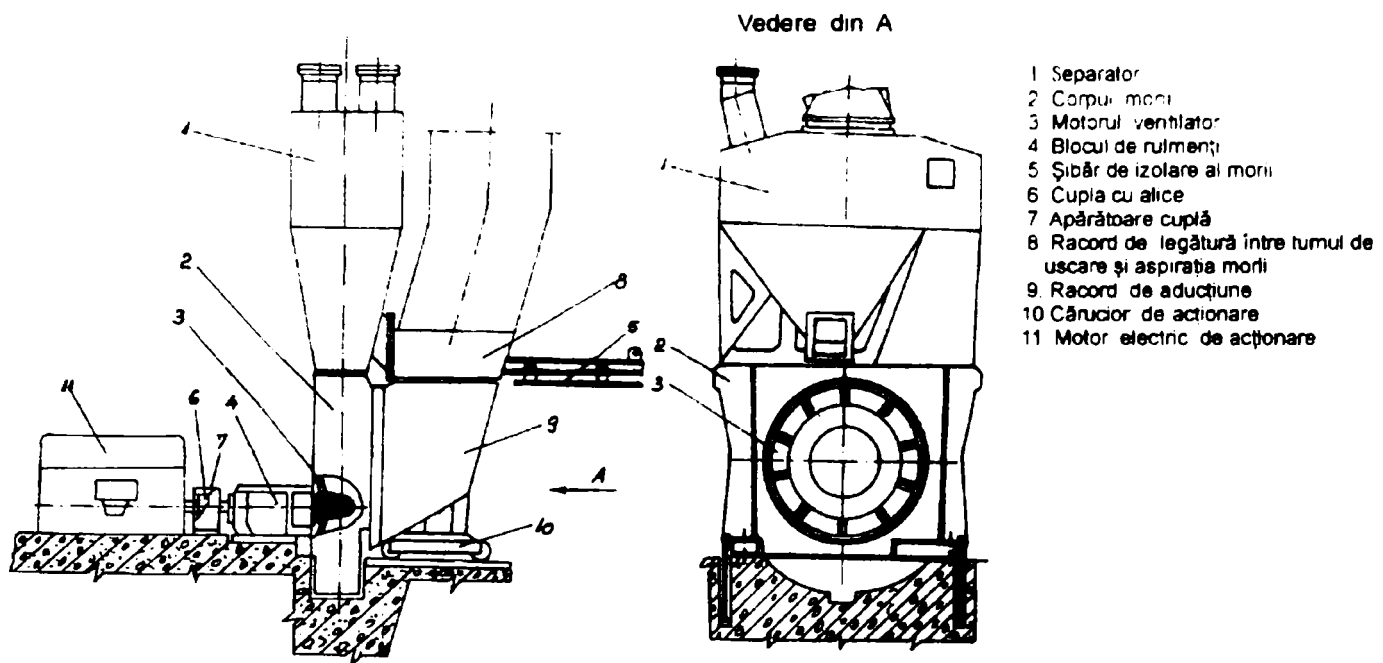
Moară ventilator tip MV 3300/800/490
